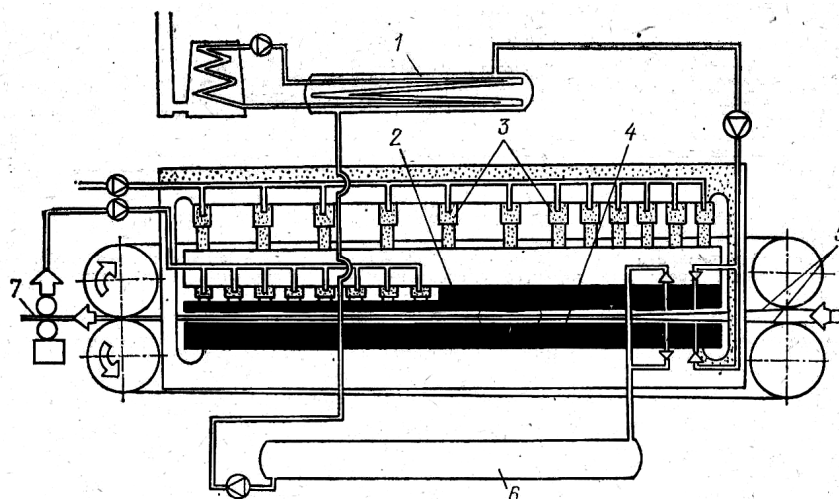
Схема ленточного пресса «Гидро-Дин»: 1 – теплообменник для нагрева смазки-теплоносителя; 2 – верхняя прессующая плита; 3 – прессующие цилиндры; 4 – нижний стол пресса; 5 – стальные ленты; 6 – сборник смазки-теплоносителя; 7 – система контроля и регулирования толщины плит
